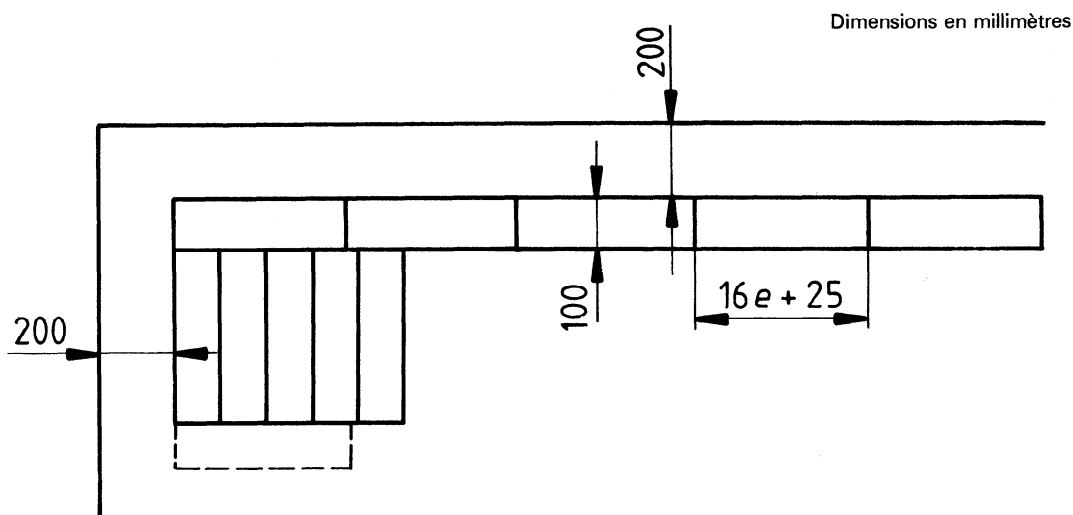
Prélèvement et dimensions des éprouvettes pour les essais mécaniques
